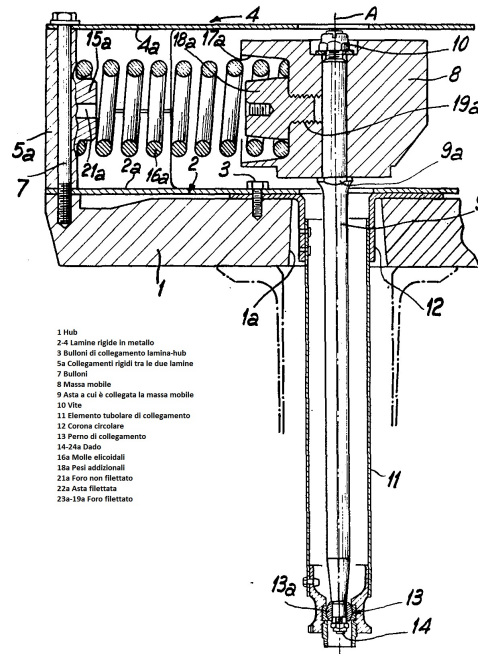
Sistema assorbimento vibrazioni 2, sezione II-II
